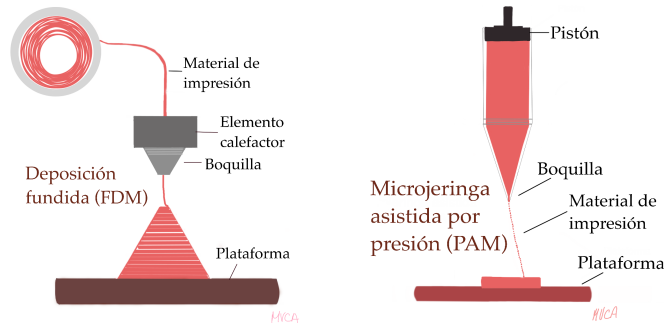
Modelos de impresión basada en extrusión. La imagen de la izquierda es un esquema de la técnica de deposición fundida (FDM) y la imagen de la derecha representa a la técnica de microjeringa asistida por presión (PAM) (2).
